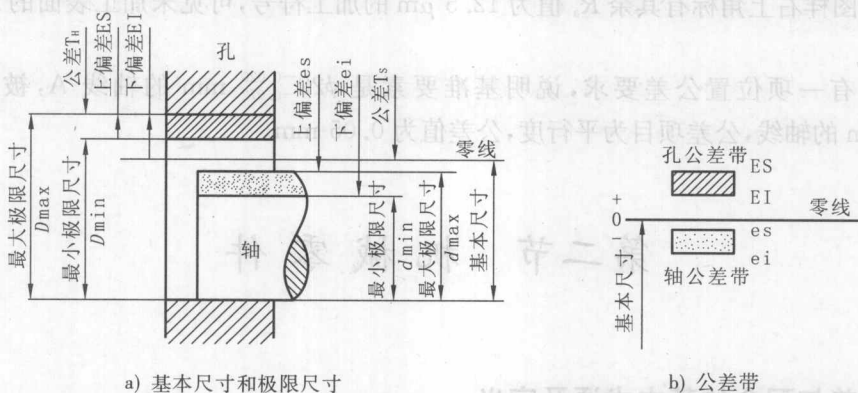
基本尺寸、极限尺寸和公差带
